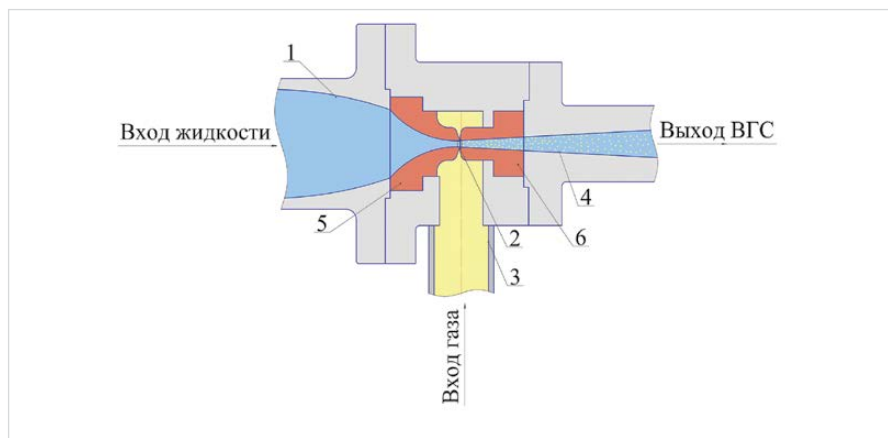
Конструкция эжектора Fig. 1 — Constructional design of the ejector
